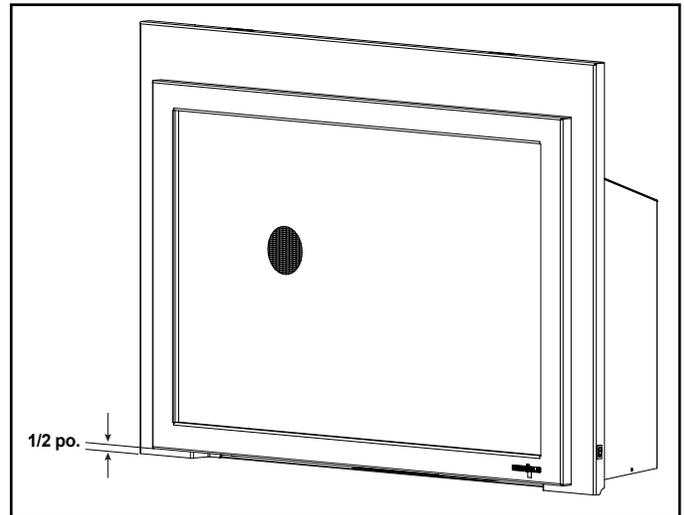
Minimum requis de 12,7 mm (1/2 po). Espace en bas de la façade
